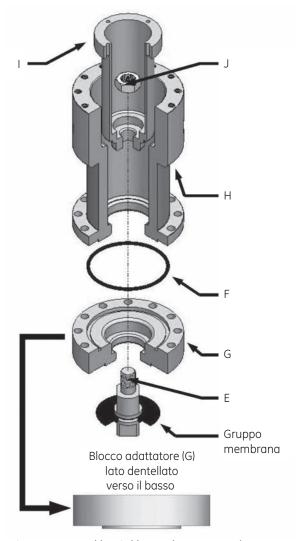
Assemblaggio blocco adattatore 1000/1500-CH
